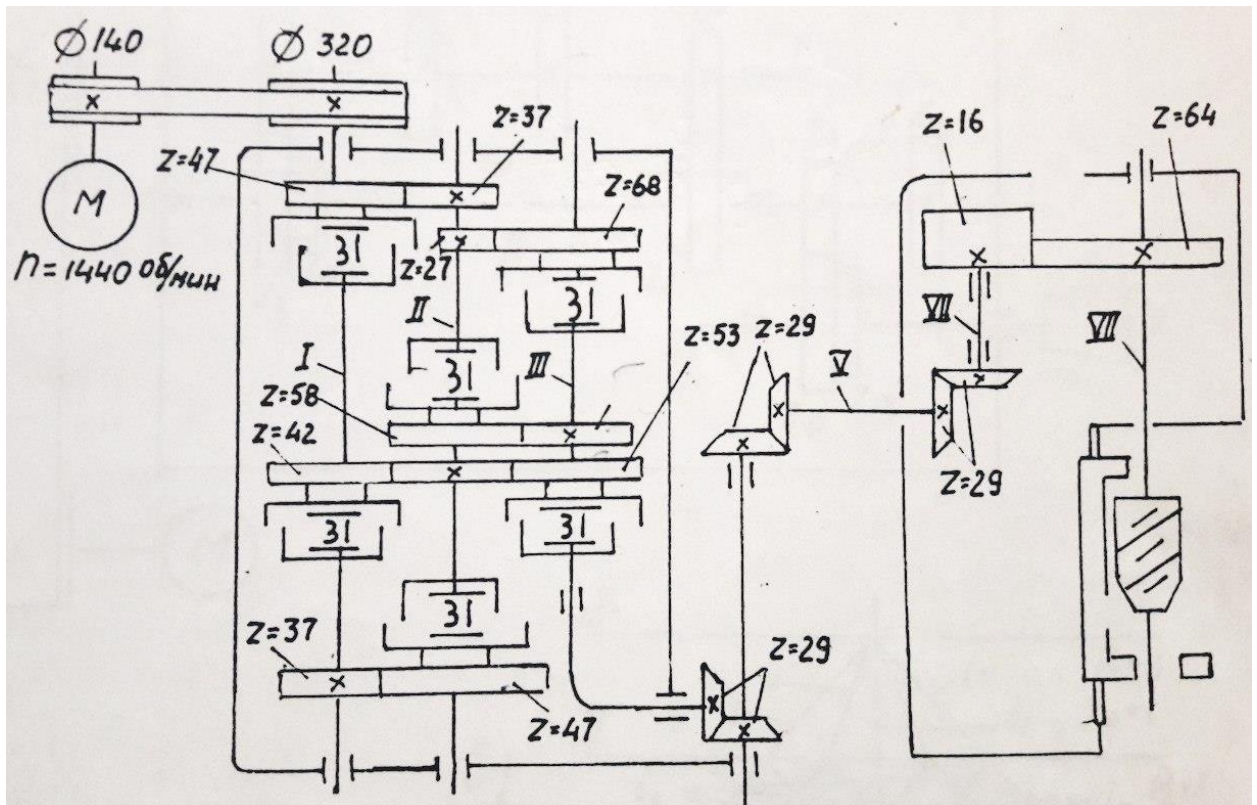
Кинематическая схема коробки скоростей зубофрезерного станка
